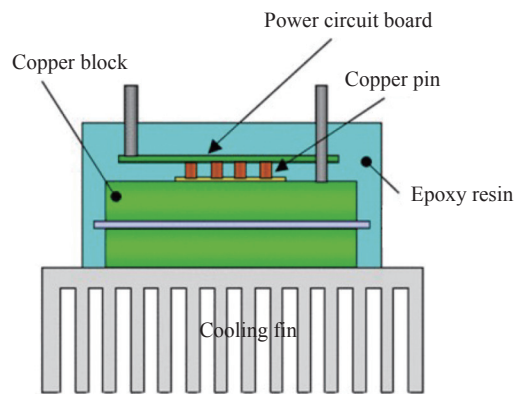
采用 PCB 板取代键合线的封装结构示意图^[5]
